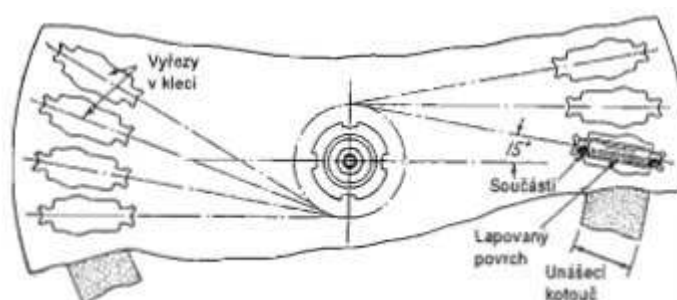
Horizontální stroj na lapování válcových ploch [9]
